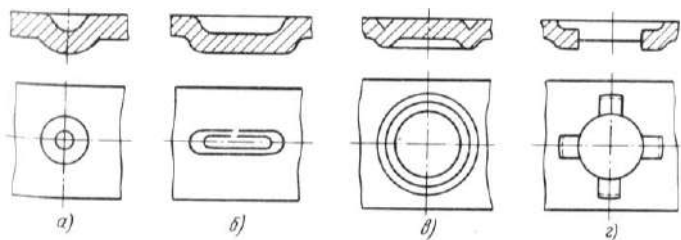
Схеми основних видів зварювальних рельєфів
